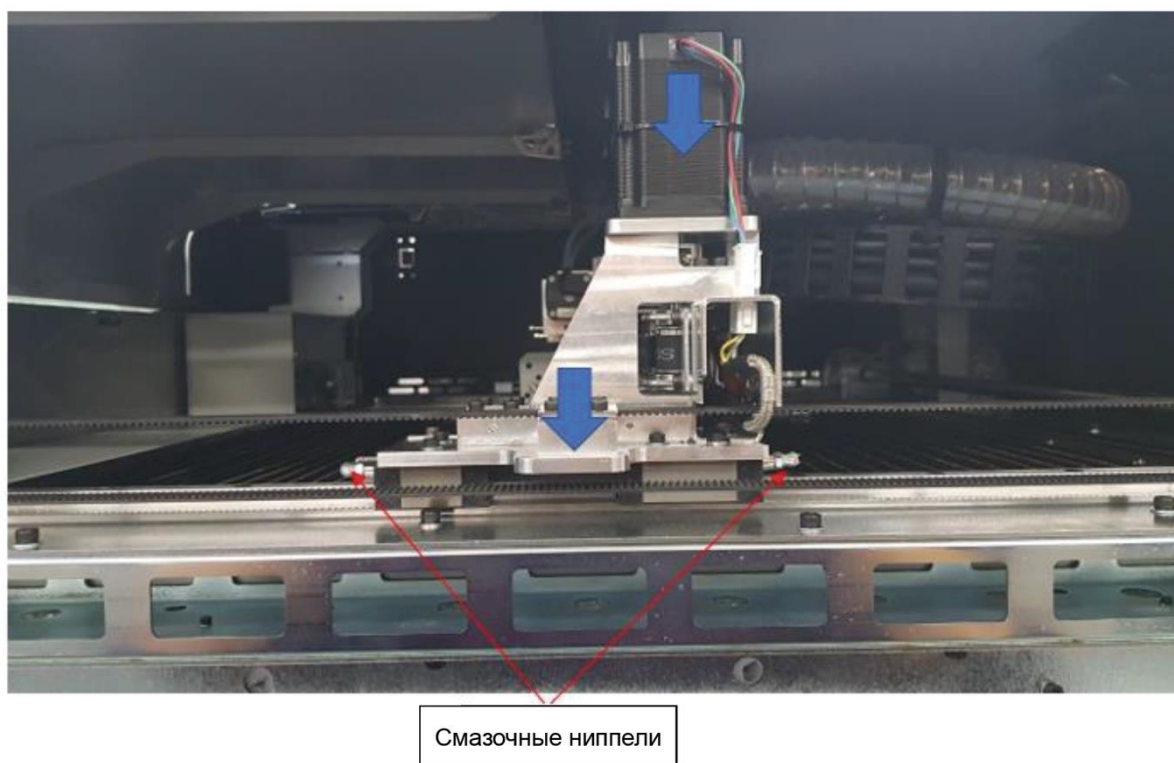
Месторасположение смазочных ниппелей в правой части принтера
